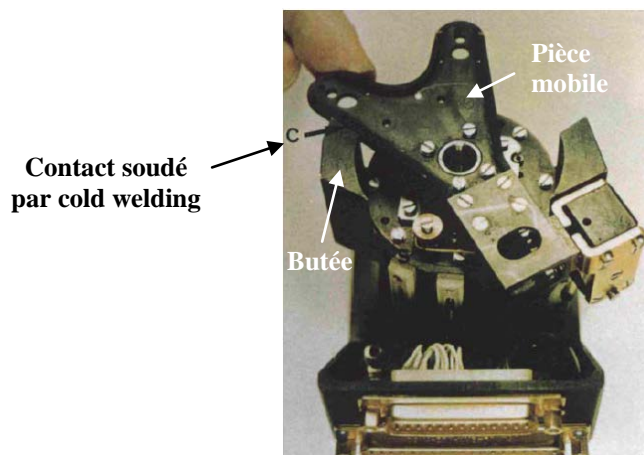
Exemple d'un dispositif de balayage ayant été victime de cold welding [42]
